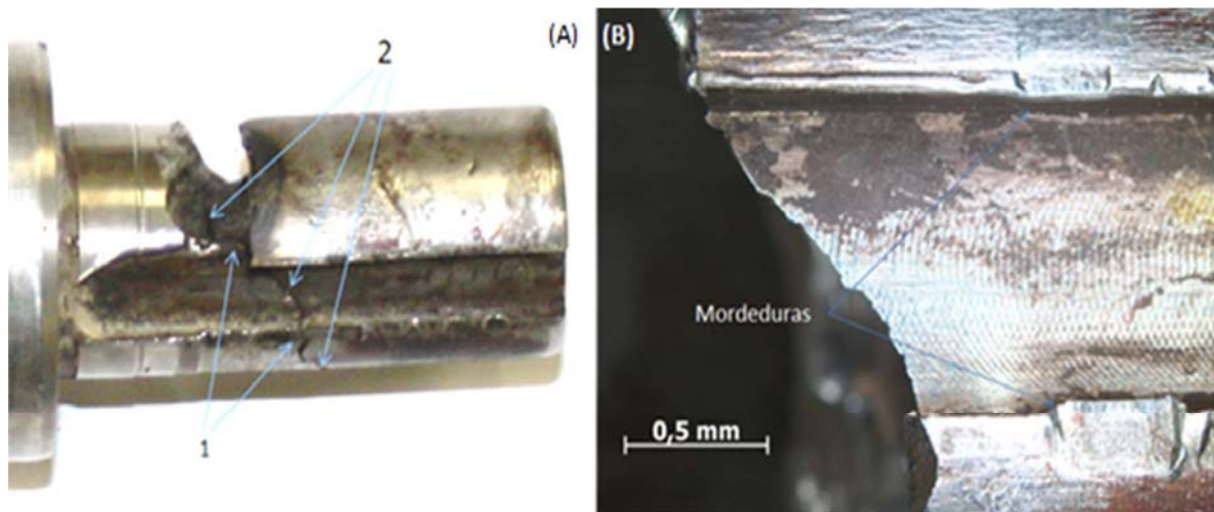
Detalhe da região de raso da chaveta. (A) direção de propagação da trinca. (B) marcas de usinagem e depressões (mordeduras) na superfície.
